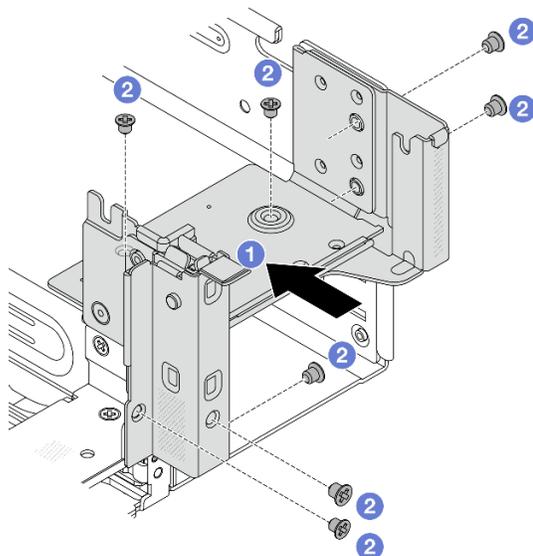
Installazione della staffa posteriore destra per il montaggio a parete
